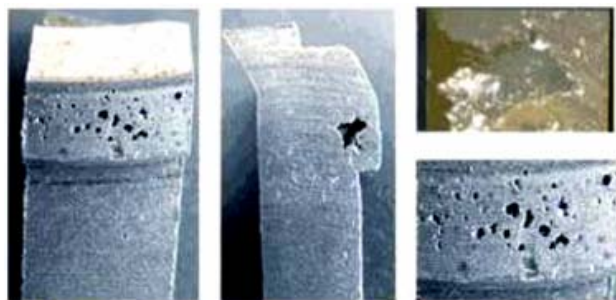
Фрагмент отливки «Крышка» с газовыми раковинами
